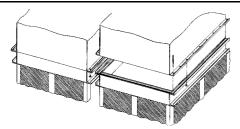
Emparejamiento de las Secciones Superiores Sobre las Secciones de Bandeja
